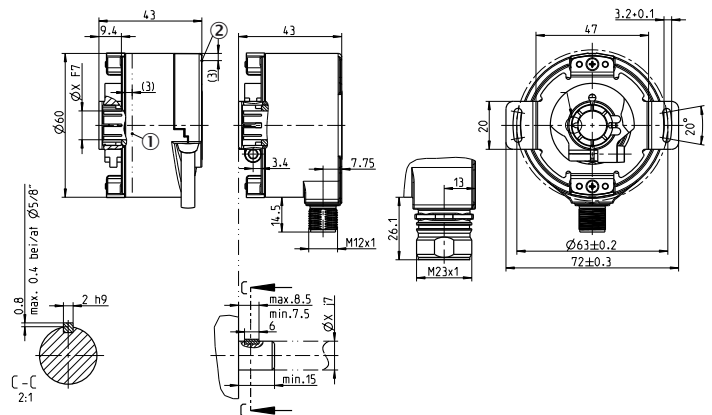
Maßzeichnung Aufsteckhohlwelle mit Leitungsabgang, Stecker M12 bzw. M23 (alle Maße in mm)
